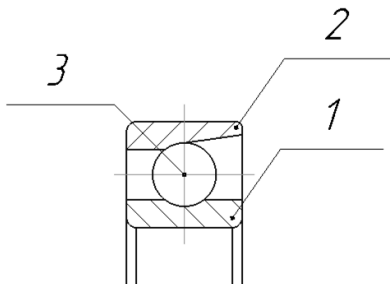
Шариковый однорядный радиально-упорный подшипник качения (ГОСТ 831-75)
